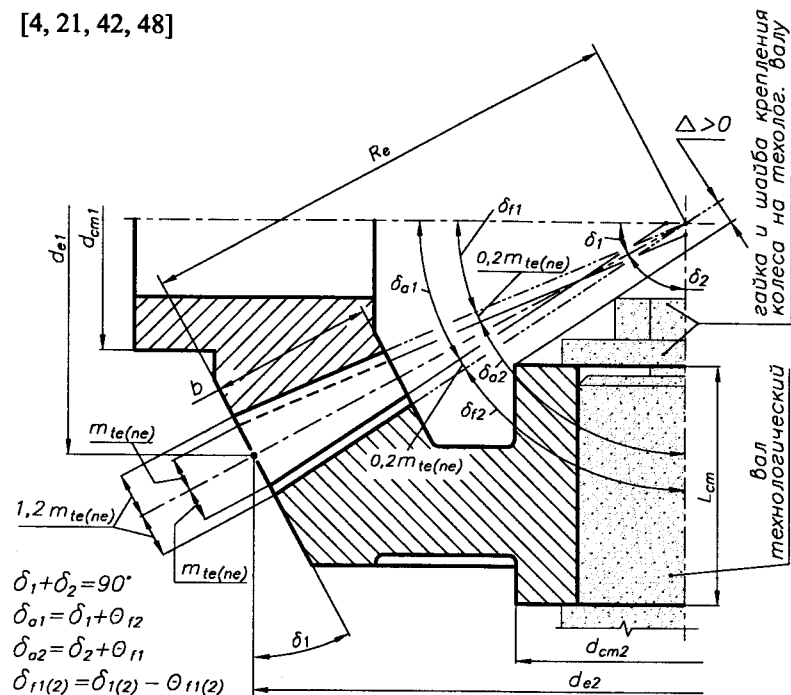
Зубчатые колеса с осевой формой зуба I и постоянным радиальным зазором по ширине зубчатого колеса
